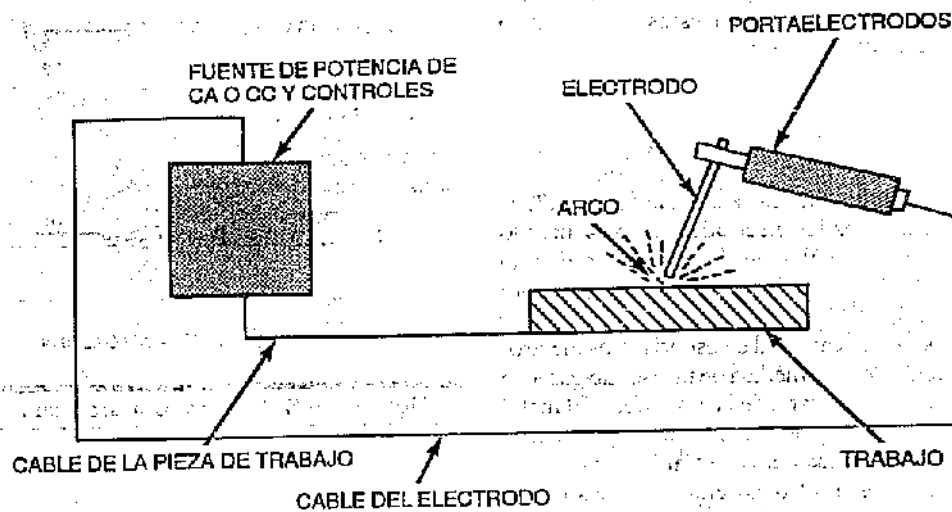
Elementos de un circuito de soldadura típico para soldadura por arco de metal protegido
